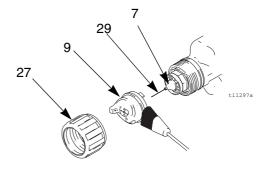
Limpieza del cabezal de aire y de la boquilla de fluido
